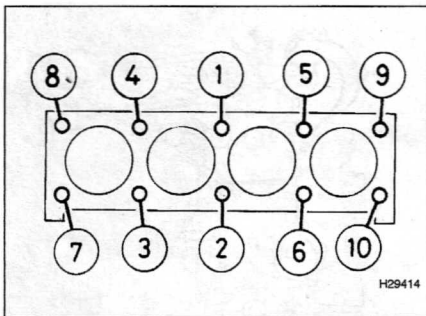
Последовательность затяжки болтов крепления головки цилиндров
